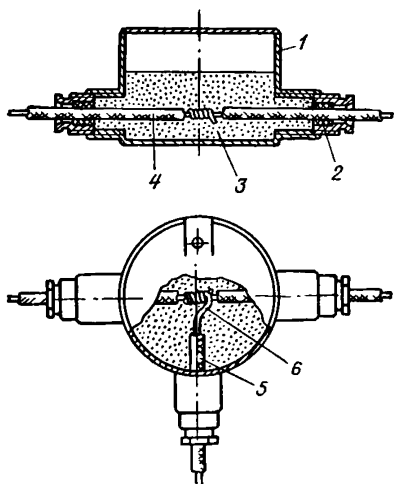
Изоляция и герметизация узла электрического соединения кабельного вывода от железокремнистого электрода с основной кабельной магистралью. 1 — фитинг ФТ-20; 2 — сальник У-50; 3 — эпоксидная смола ЭД-16; 4 — кабель АВРГ 1×10 (ГОСТ 433—58); 5 — кабельный вывод от железокремнистого электрода; 6 — контактное соединение.
